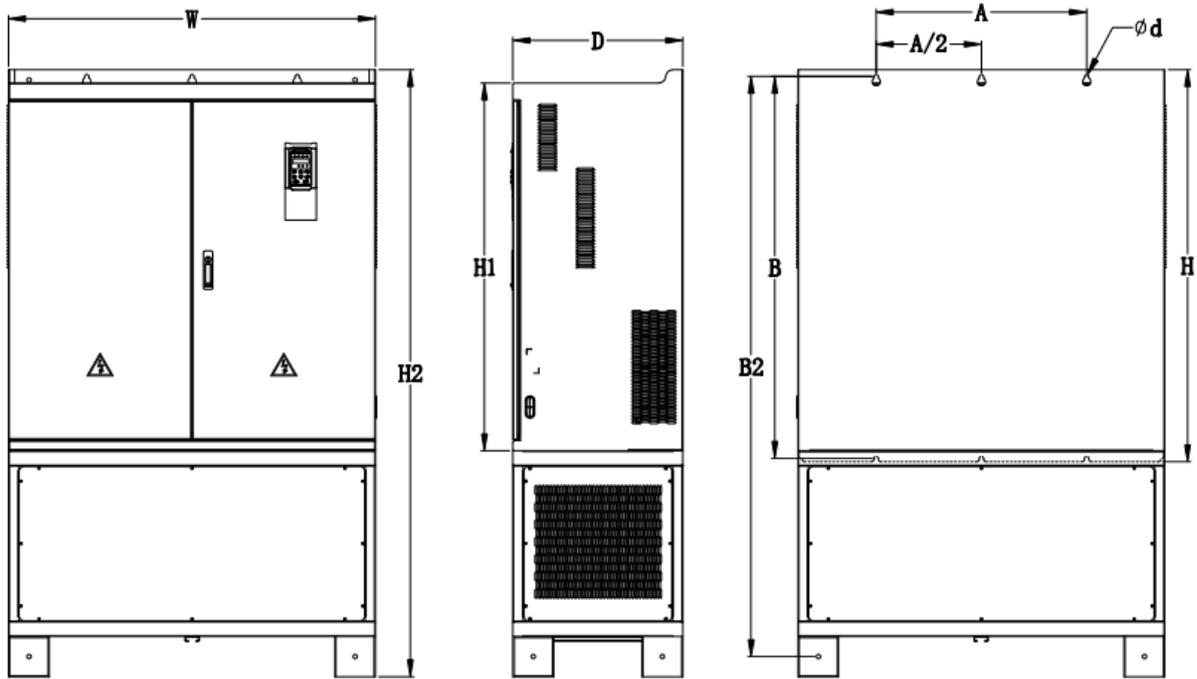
Dimensiones del TAMAÑO K ~ O (315KW-710KW)
